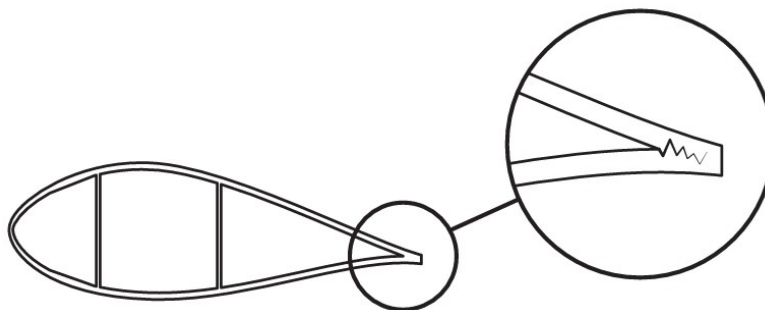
Fissuras de fadiga na borda de fuga [19].
